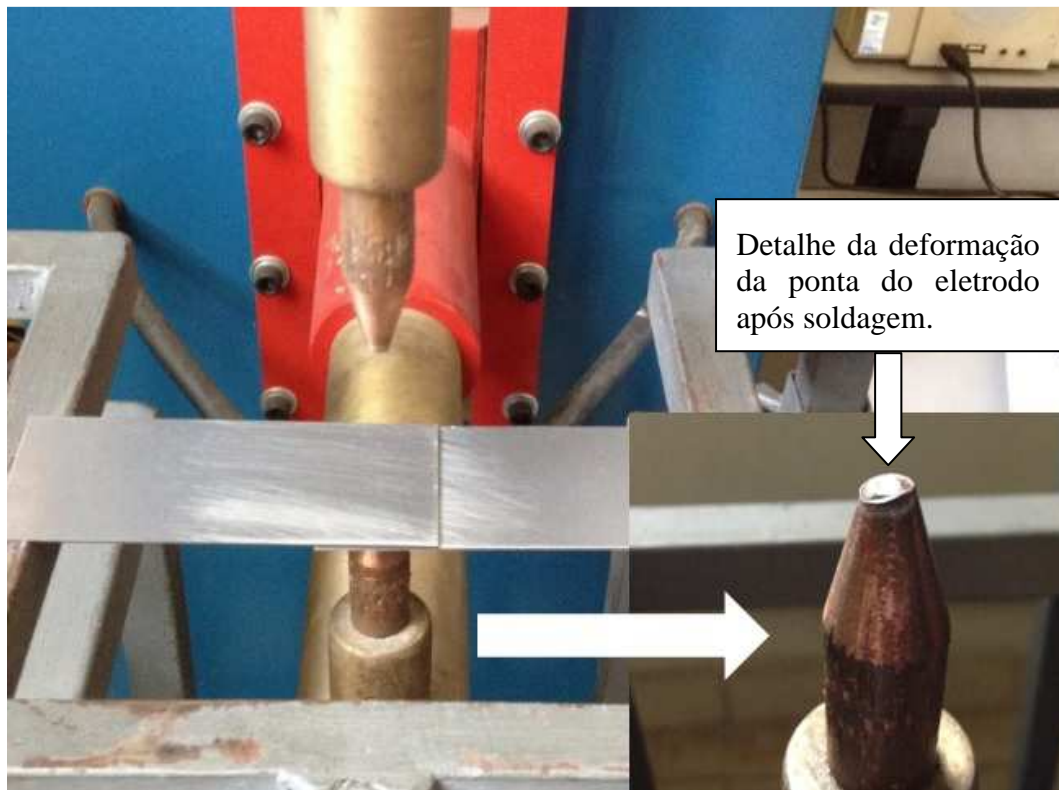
Montagem de uma junta com detalhe do eletrodo deformado após a soldagem.
